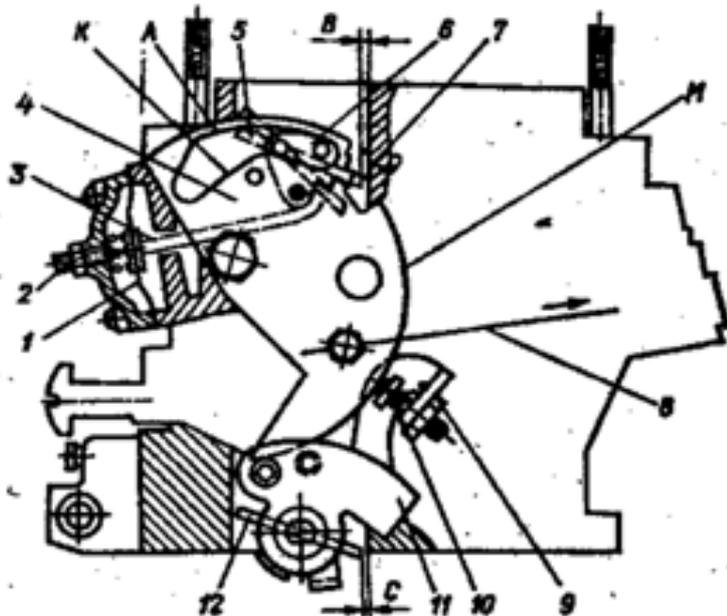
Пусковое устройство карбюратора: 1 - диафрагма; 2 - регулировочный винт; 3 - шток диафрагмы; 4 - рычаг управления воздушной заслонкой; 5 - воздушная заслонка; 6 - рычаг воздушной заслонки; 7 - возвратная пружина воздушной заслонки; 8 - тяга рукоятки привода воздушной заслонки; 9 - стопор регулировочного винта; 10 - регулировочный винт приоткрывания дроссельной заслонки первой камеры; 11 - рычаг управления дроссельными заслонками; 12 - дроссельная заслонка первой камеры; К - нижний профиль паза рычага 4 для ограничения максимального приоткрывания воздушной заслонки; А - верхний профиль паза рычага 4, обеспечивающий механическое открытие воздушной заслонки; М - кромка рычага 4 для обеспечения пускового зазора дроссельной заслонки первой камеры
